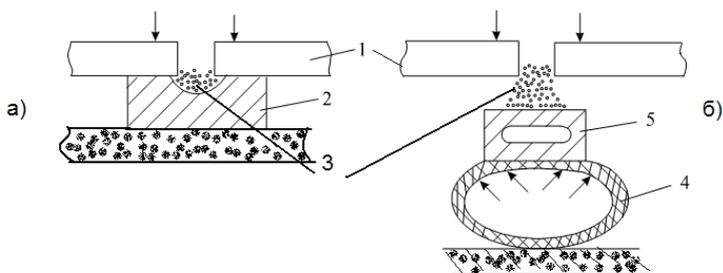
Схема сварки на флюсо-медной подкладке: *а* – на жесткой флюсо-медной подкладке; *б* – на флюсо-медной водоохлаждаемой подкладке (*1* – изделие; *2* – подкладка с канавкой; *3* – слой флюса; *4* – пневматический шланг; *5* – водоохлаждаемая подкладка)
